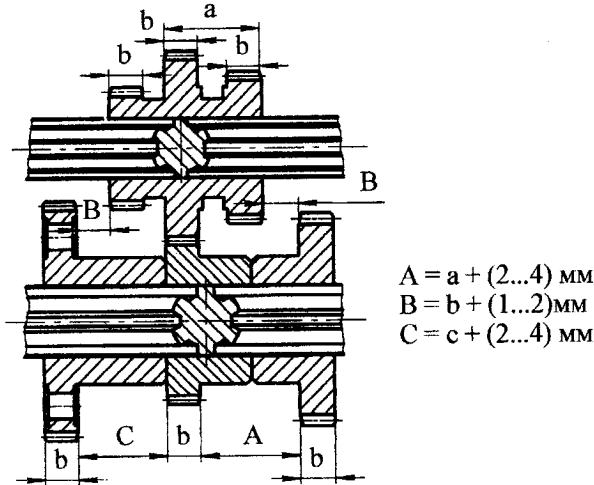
Лінійне розташування нерухомих зубчастих коліс
